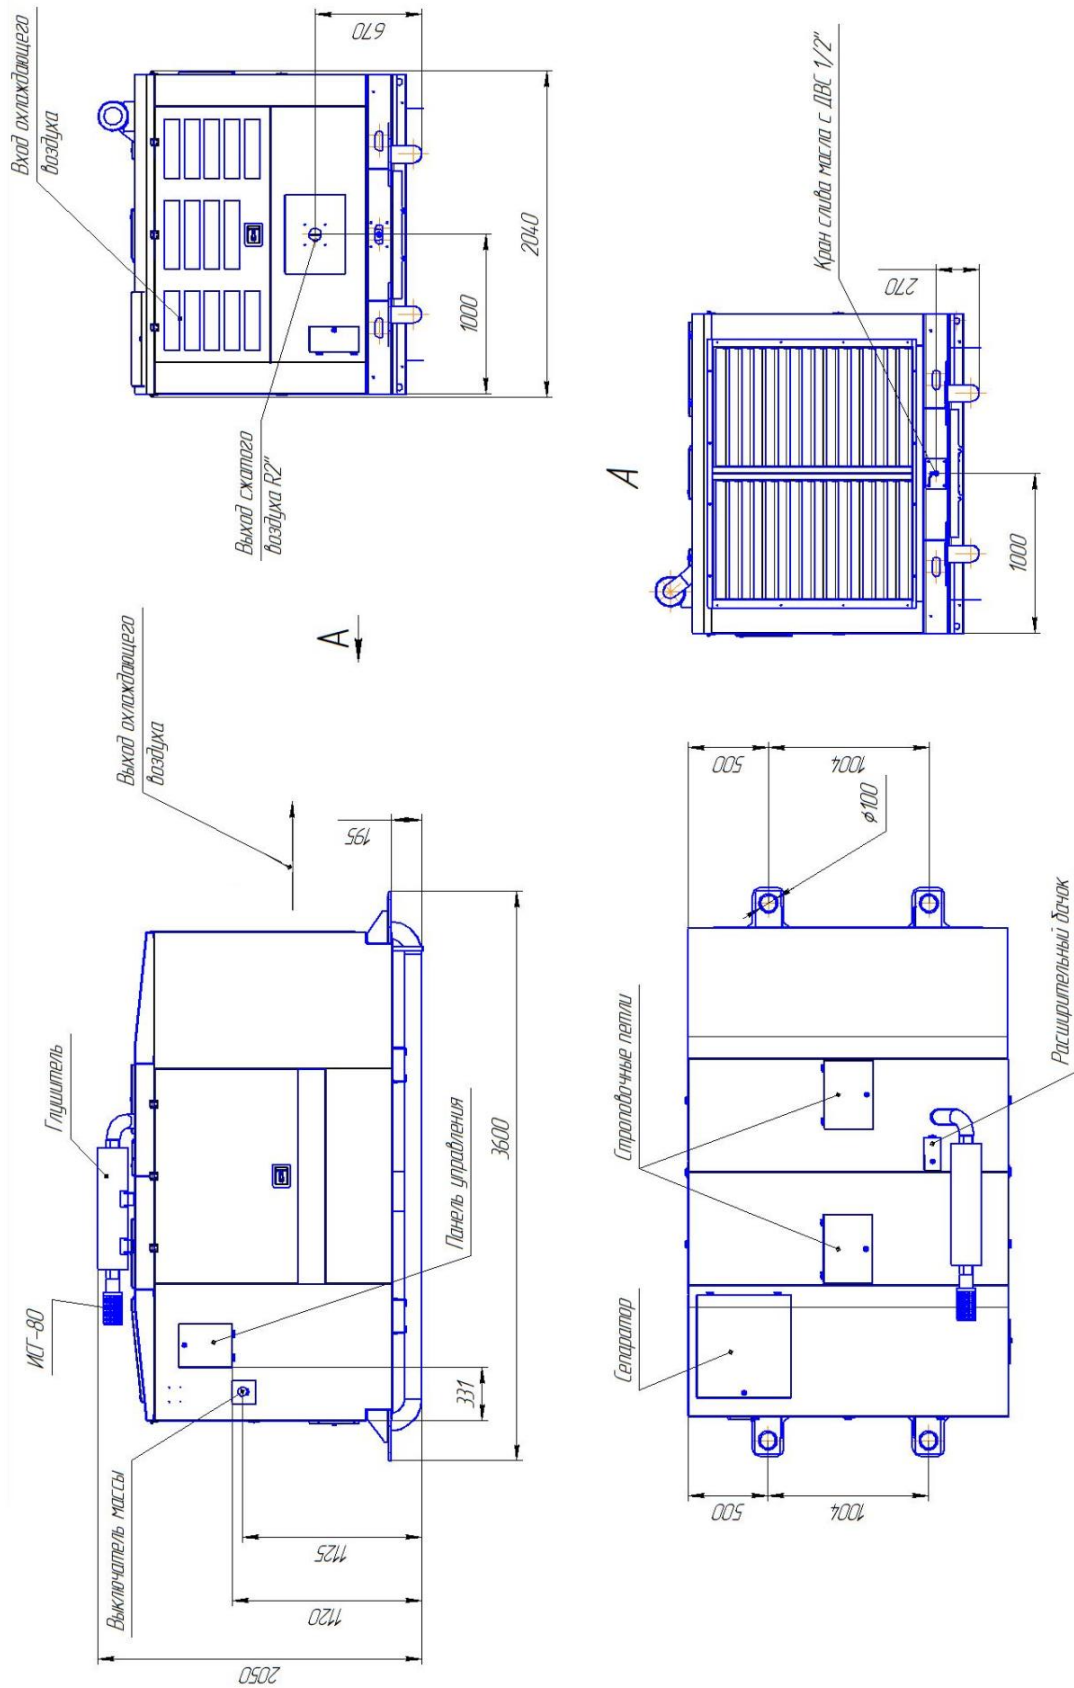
Габаритный чертёж компрессорной установки KV-20/12
